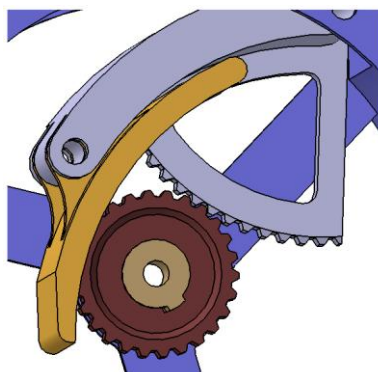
Engrenamento centrado. É possível ver na figura o engrenamento entre a roda dentada e o braço de transmissão.
